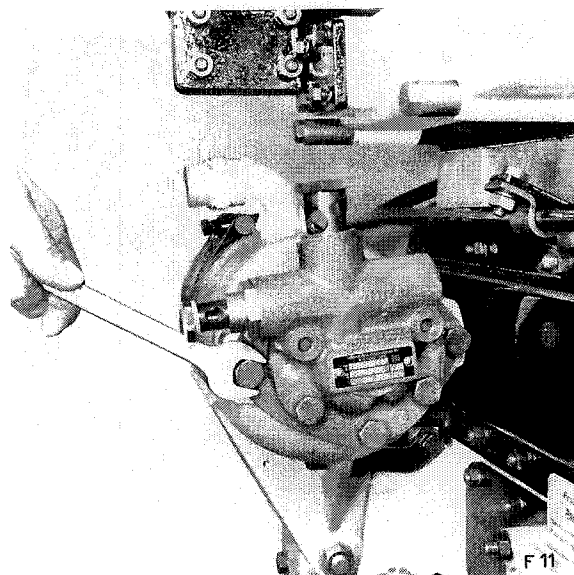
Lösen der Befestigungsschrauben an der Hochdruckpumpe
